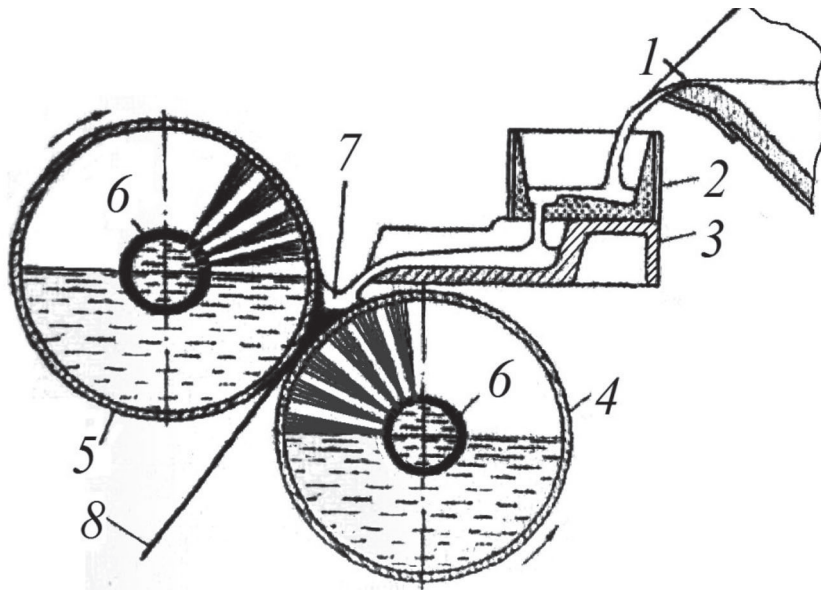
Схема процесса получения листа на валковой разливочной установке [2]: 1 – ковш с жидким металлом; 2 – чаша; 3 – лотковый питатель; 4 – валок с приводом; 5 – валок без привода; 6 – охлаждающая вода; 7 – расплав; 8 – лист
